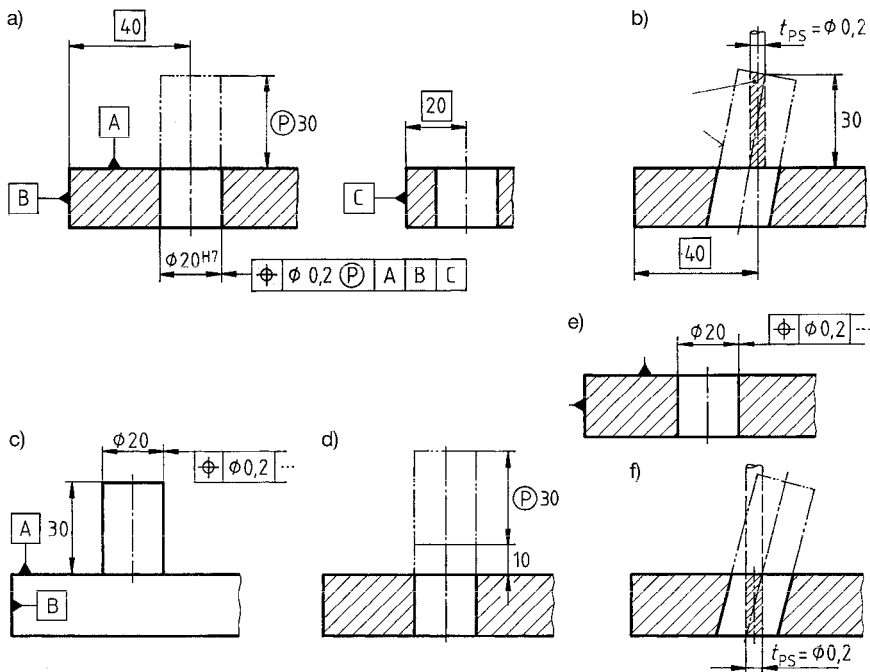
Projizierte Toleranzzone bei einer Positionstolerierung. a) Zeichnung, b) Toleranzzone und zulässige Lage der Bohrungsachse, c) Feinguss-Massivteil zum Vergleich, d) noch weiter verschobene Toleranzzone; e) Positionstolerierung der Bohrung ohne projizierte Zone, f) zulässige Lage der Bohrung dazu
